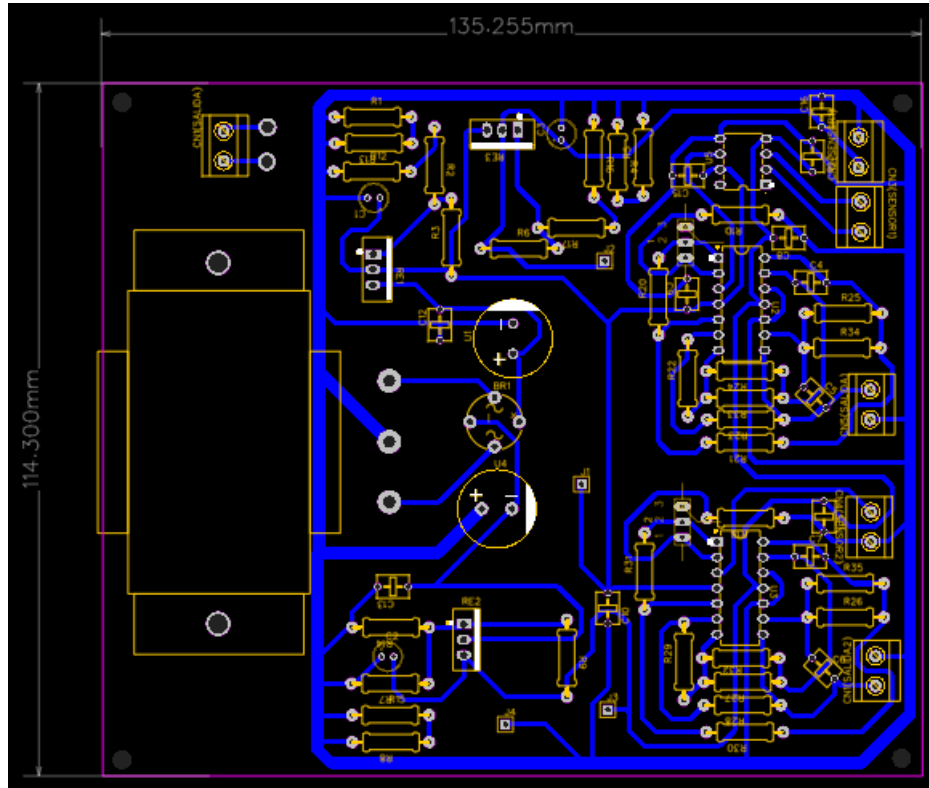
Diseño de la PCB (EasyEDA - Online PCB Design & Circuit Simulator, 2025)
